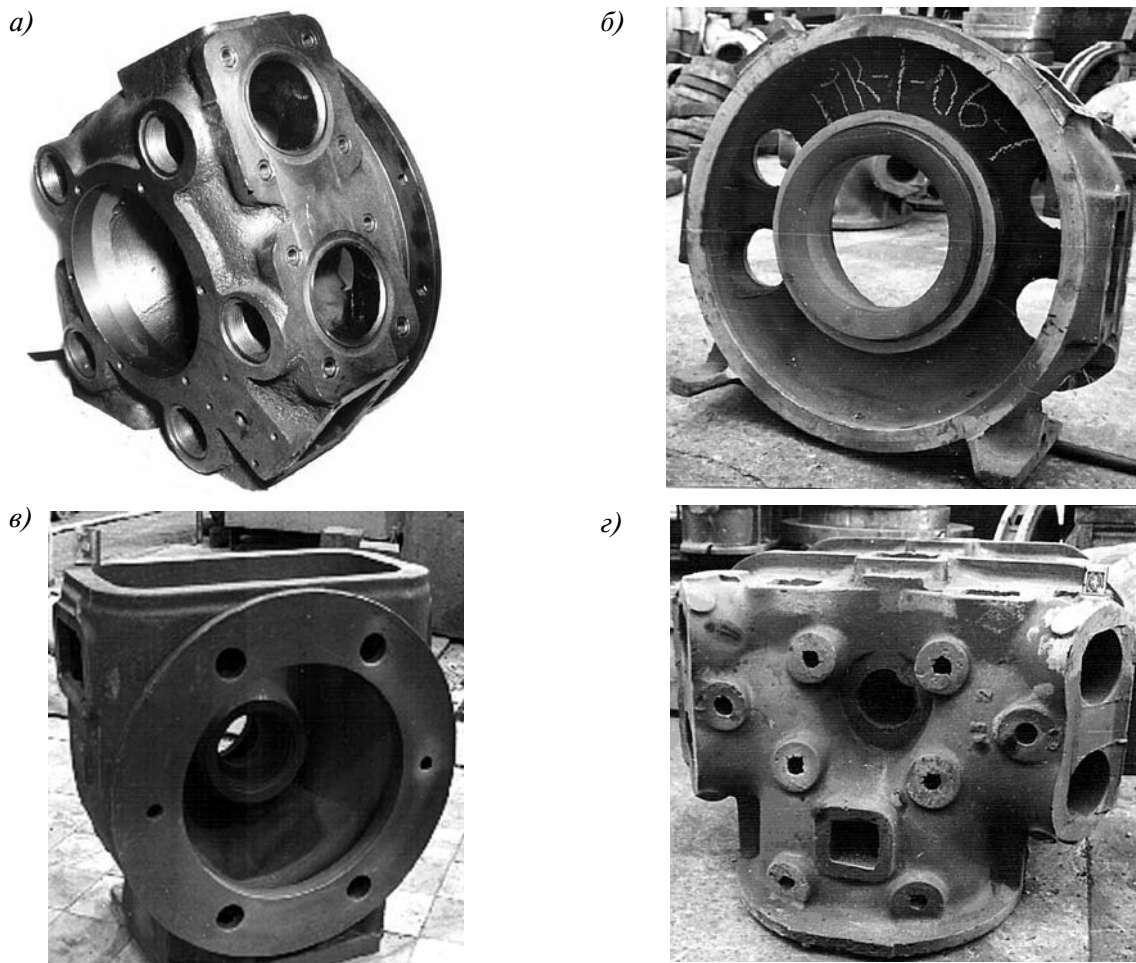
Корпуса турбокомпрессоров из ЧВГ35.
